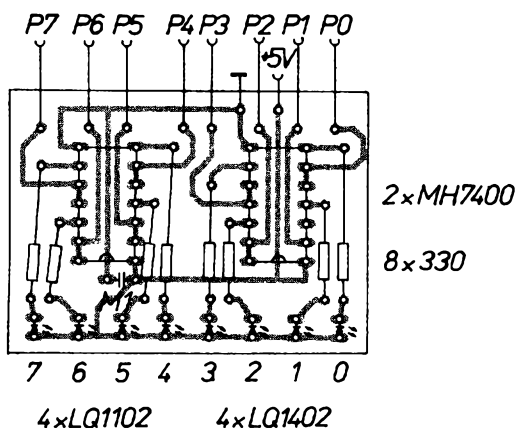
Obrazec plošných spojů desky základní jednotky X 503
